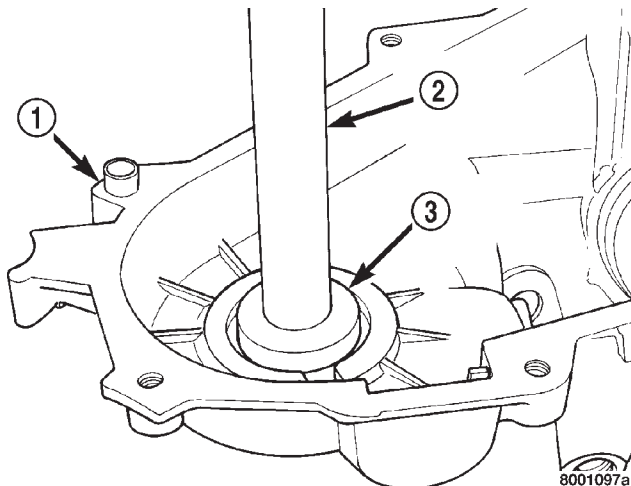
Desmontaje del cojinete del eje transmisor delantero
